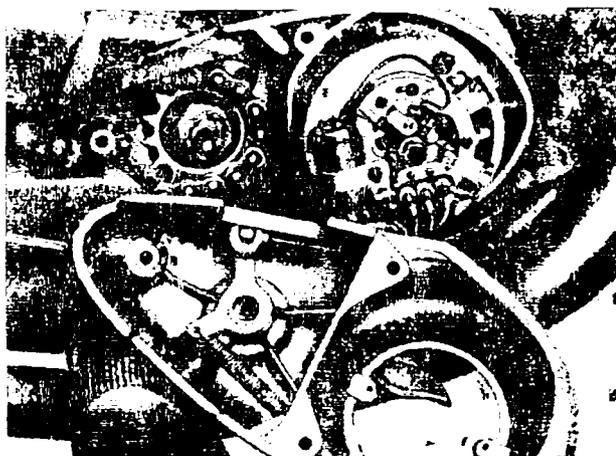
Abdeckkappe bei RT 125 abgenommen, um zum Antriebskettenrad am Getriebe zu gelangen
